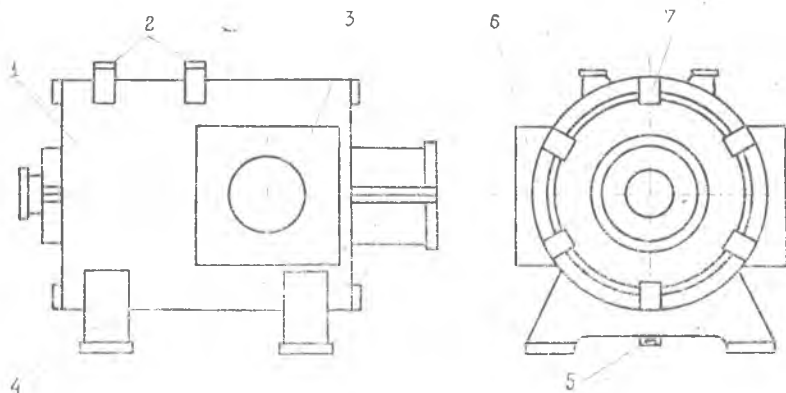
Внешний вид нагнетателя: 1 — корпус; 2 — опоры аккумулятора; 3 — патрубок нагнетательный; 4 — лапы опорные; 5 — направляющие; 6 — патрубок газопримный; 7 — кронштейн
